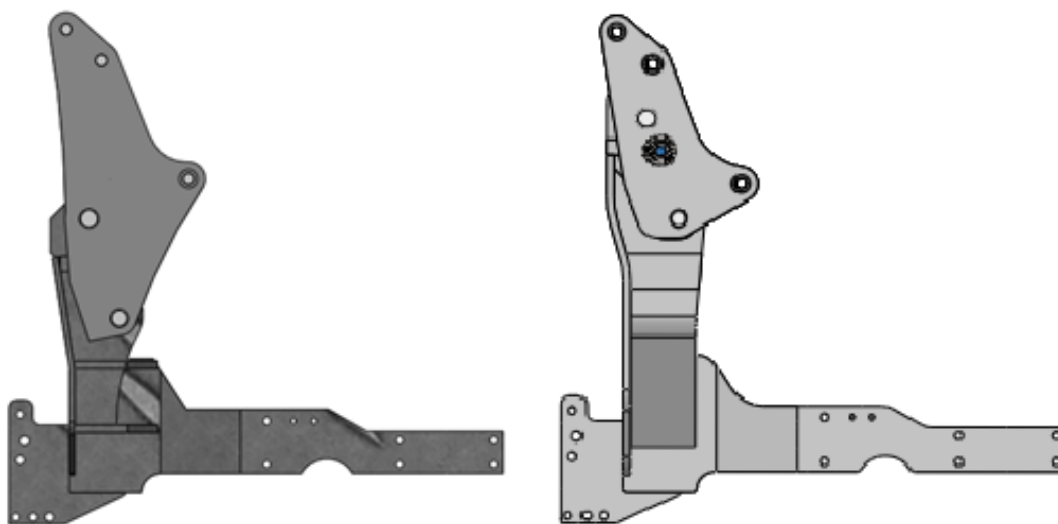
Conjunto de amarre + pilarete antiguo/nuevo.
